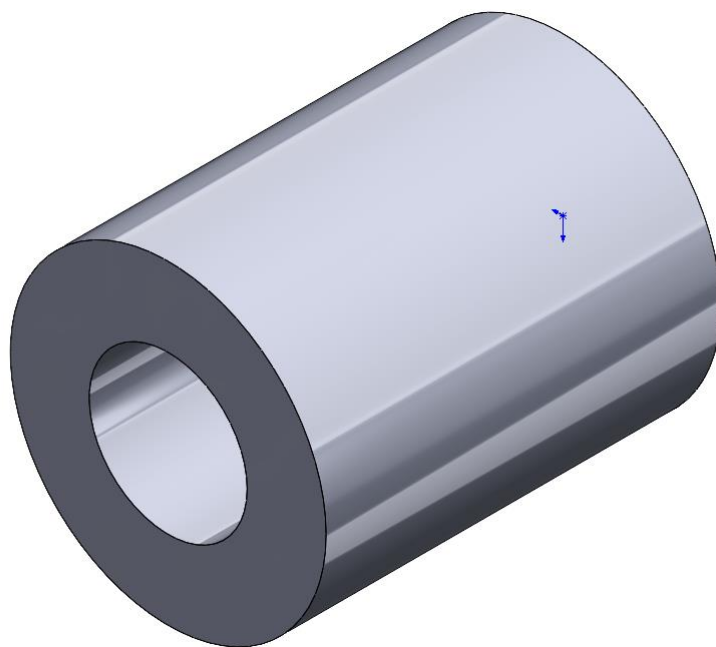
Деталь 4А.0003.007 Втулка Балки
